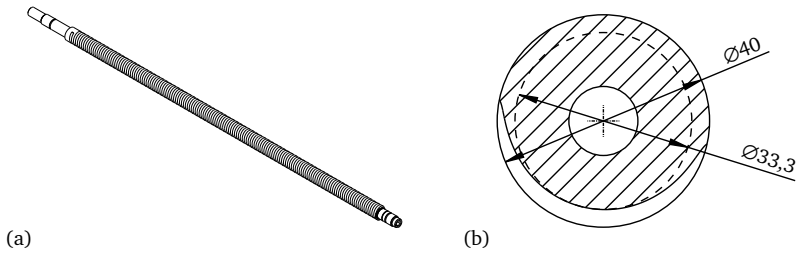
Betrachtete Spindelwelle mit 1404,5 mm Länge (a) sowie zugehöriger Querschnitt des Spindelteils mit Außen- und Kerndurchmesser (b)
